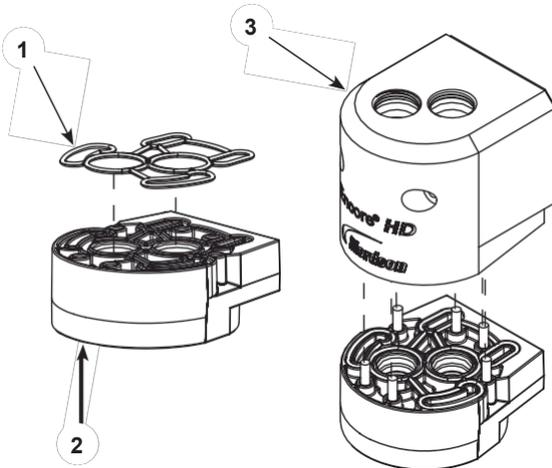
Assemblaggio del blocco Y inferiore al collettore di spurgo
